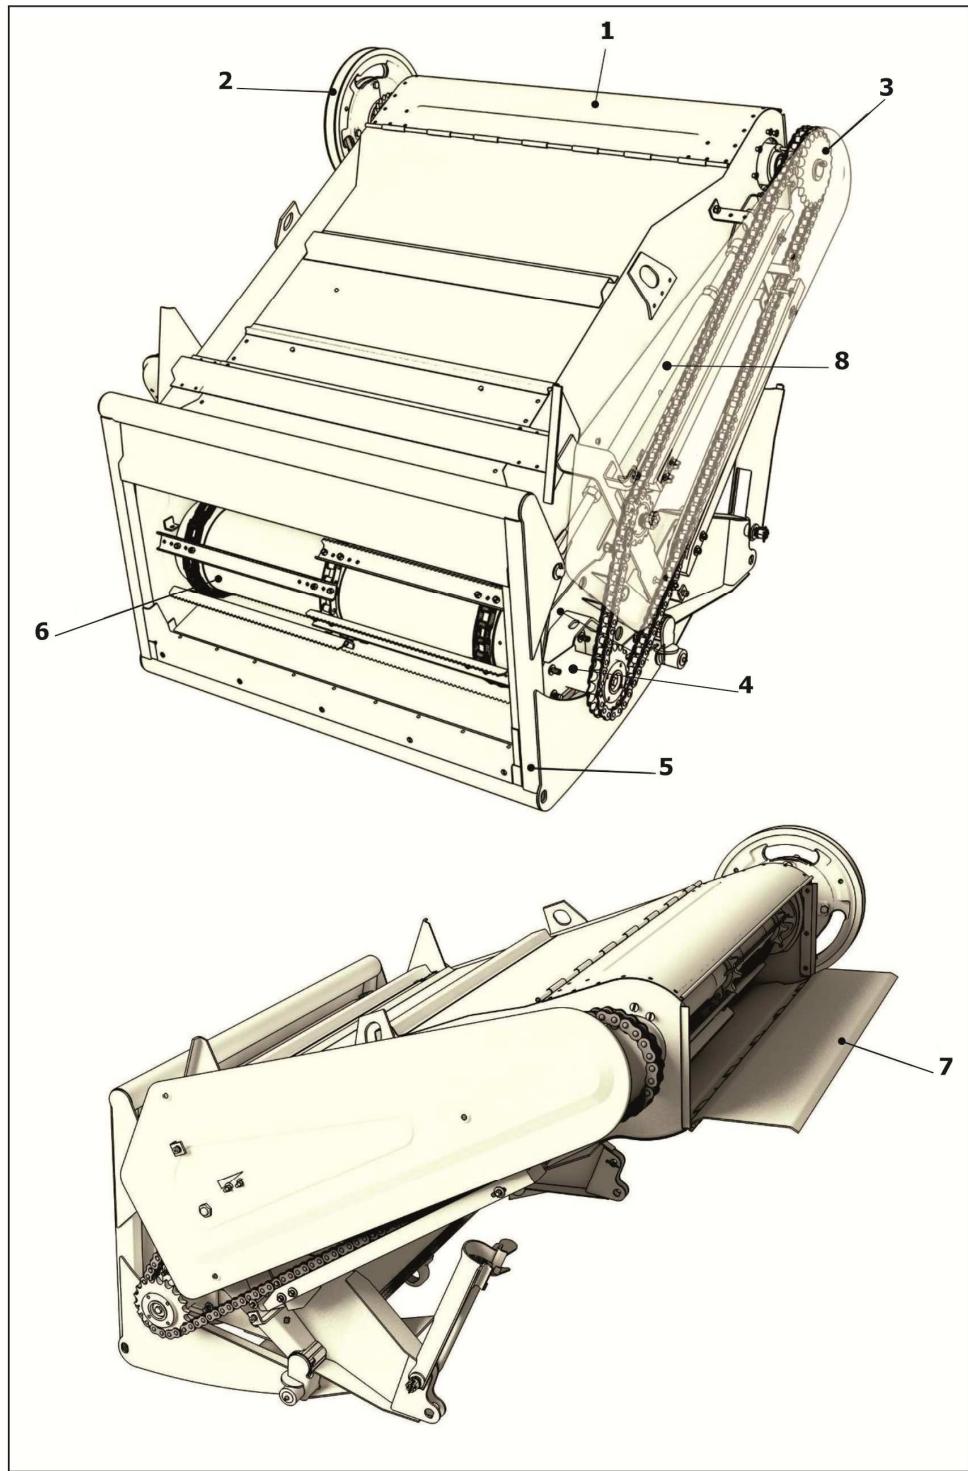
Механическая регулировка отрывочных пластин русла
